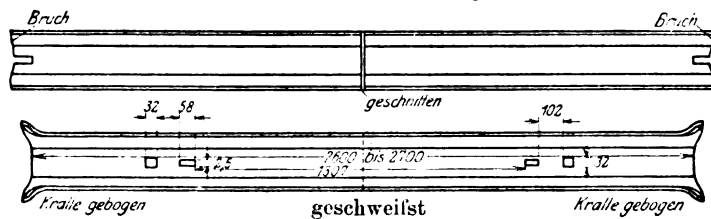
Schmelzschweißung eiserner Querswellen.
